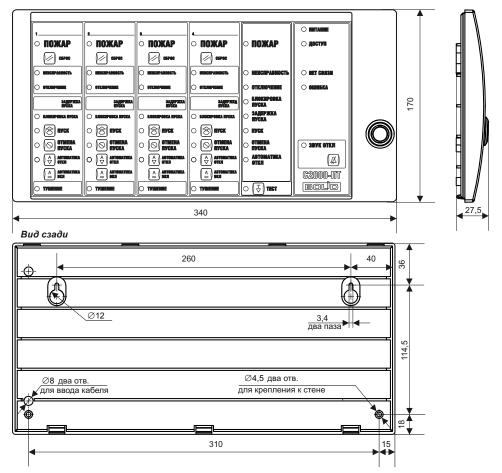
Внешний вид, габаритные и установочные размеры блока «С2000-ПТ»
